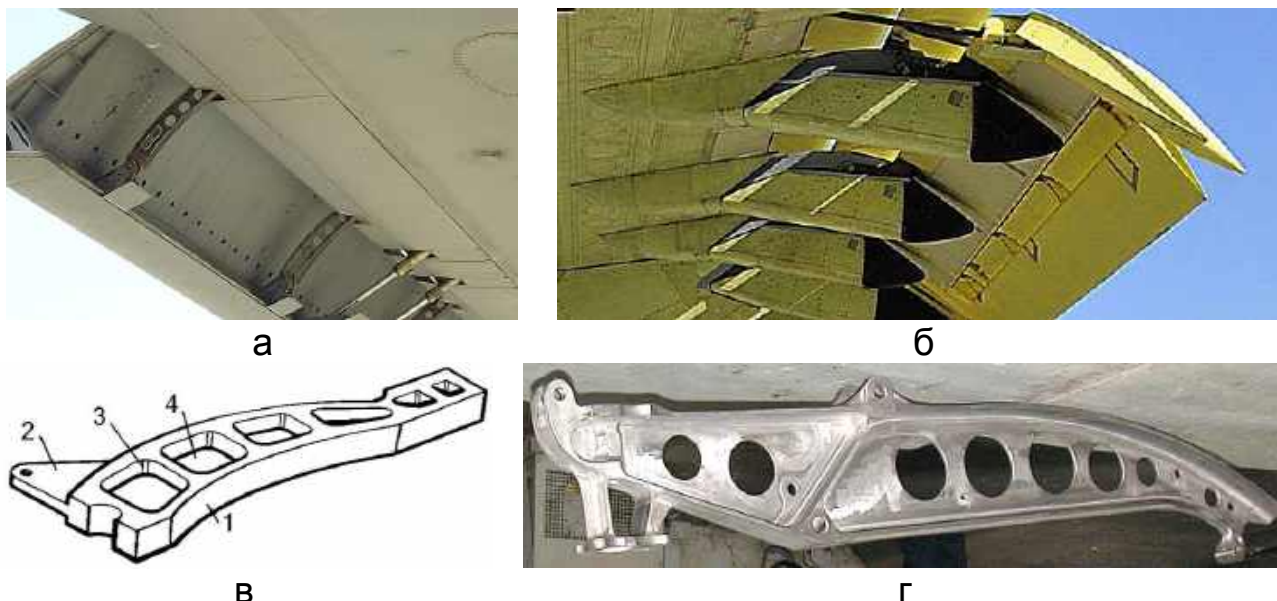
Рейки механізації крила: а – передкрилка; б – закрилка; в – типова конструкція; г – зовнішній вигляд рейки закрилка; 1 – зовнішній контур; 2 – площина вушка; 3 – внутрішні контури колодязів; 4 – дно колодязів
